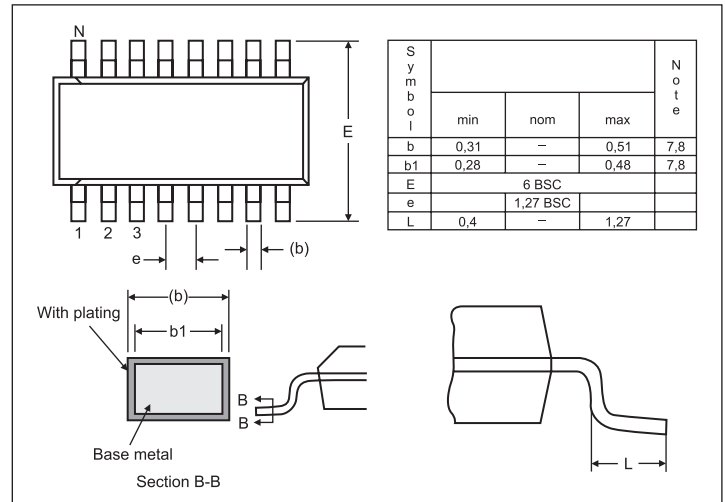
Размеры JEDEC-корпуса (типичный образец)
